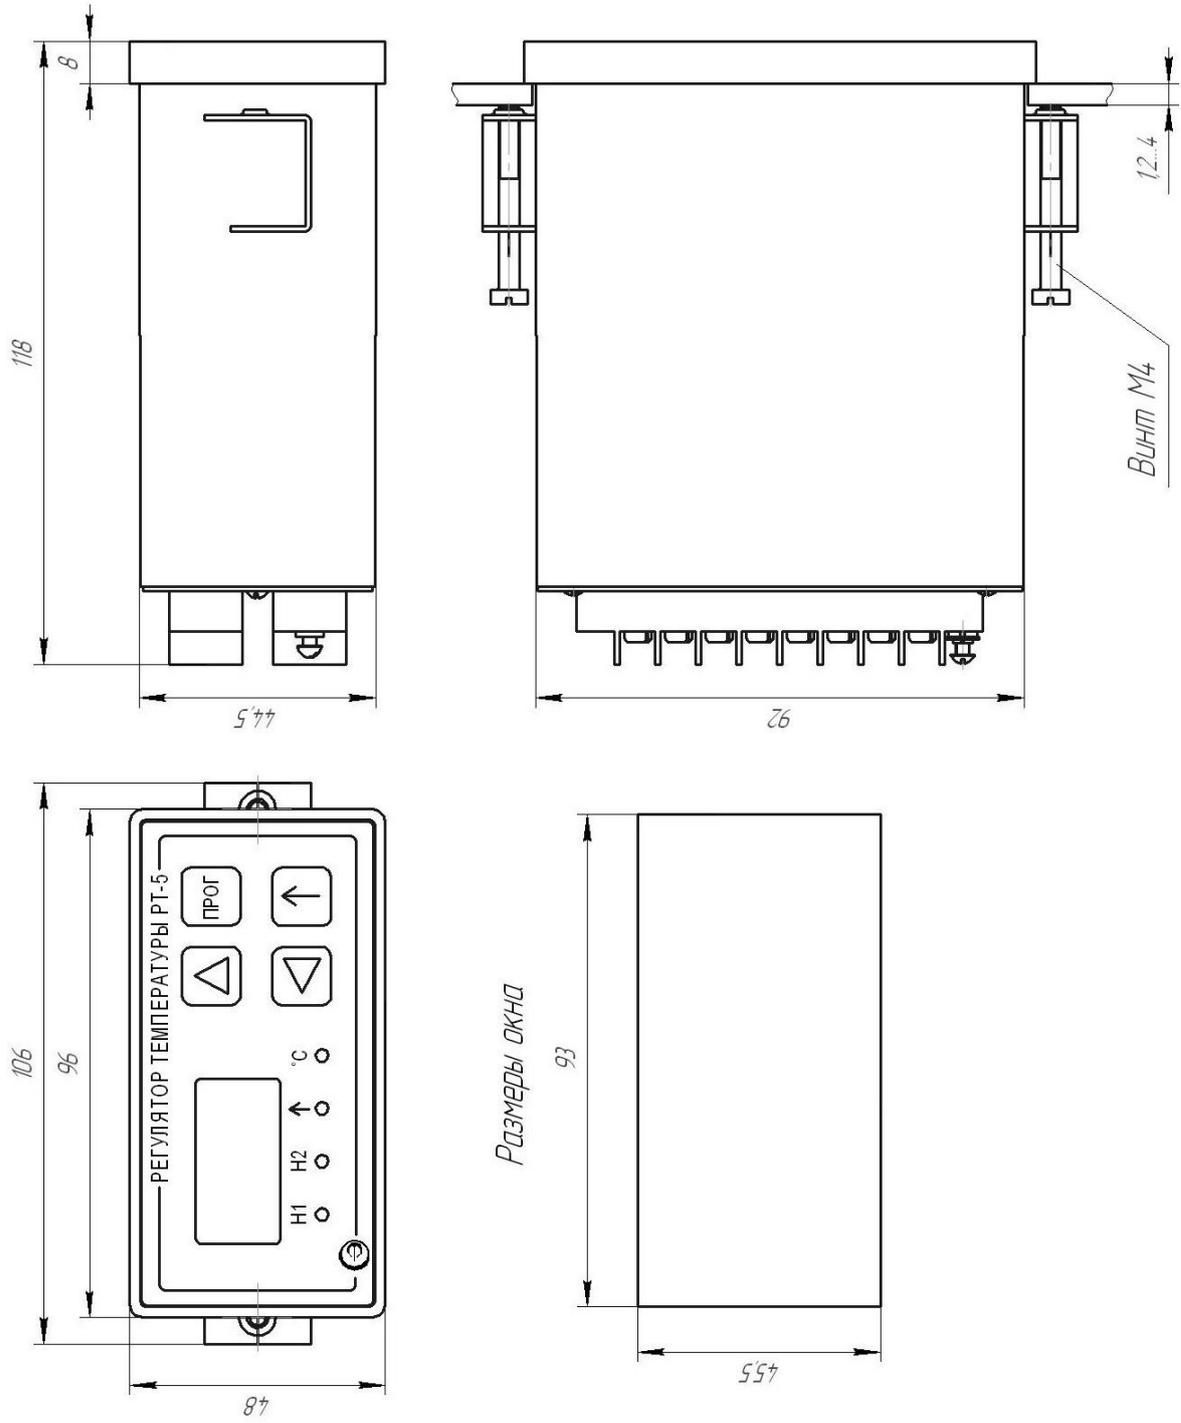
Габаритные и установочные размеры регулятора щитового испол-
